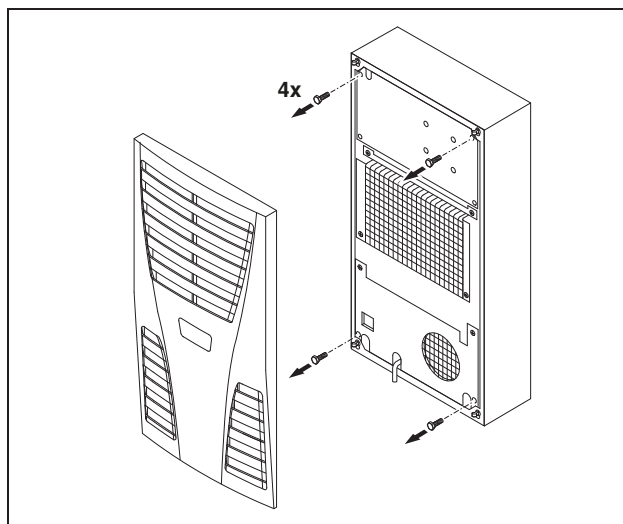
Gäller endast 3302.xxx: Ta bort fyra skruvar
